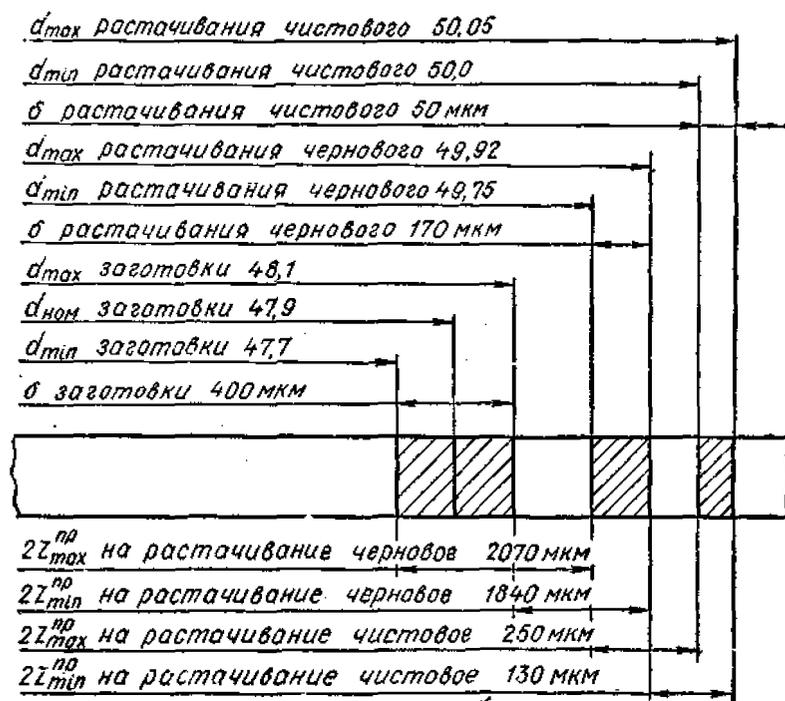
Схема графического расположения припусков и допусков на обработку отверстия $\varnothing 50^{+0,05}$ корпуса (рис. 14)
